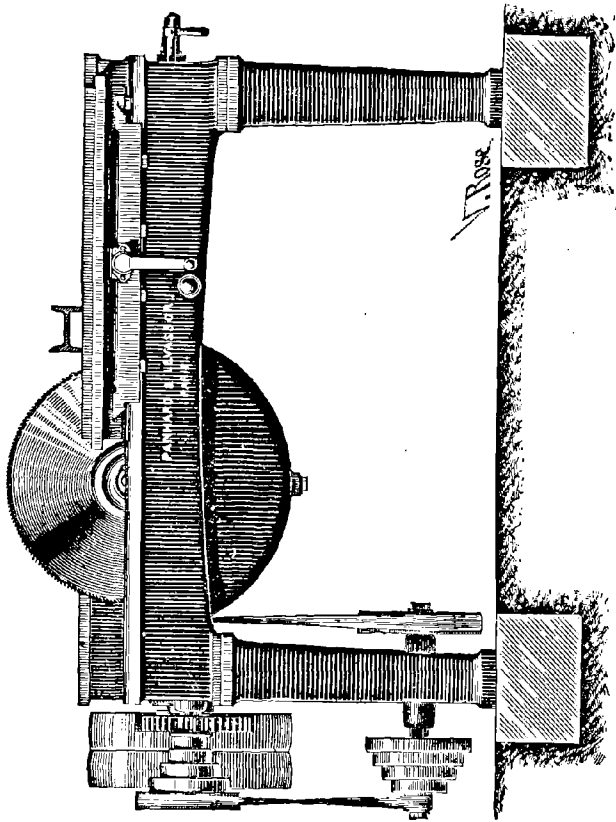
Scie circulaire Panhard et Lovassor. — Vue de côté.
